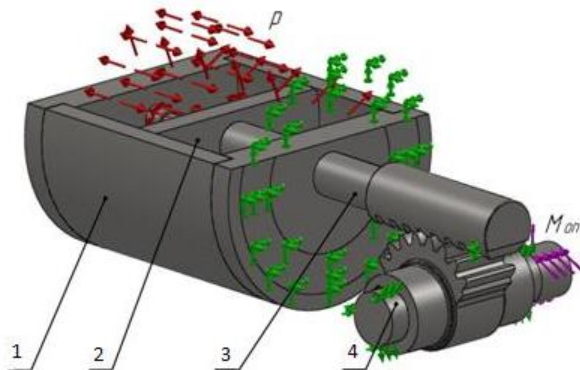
Твердотільна модель механізму повороту кульового крана: 1 – корпус циліндра, 2 – поршень, 3 – шток-рейка, 4 – вал з зубчатым сегментом
